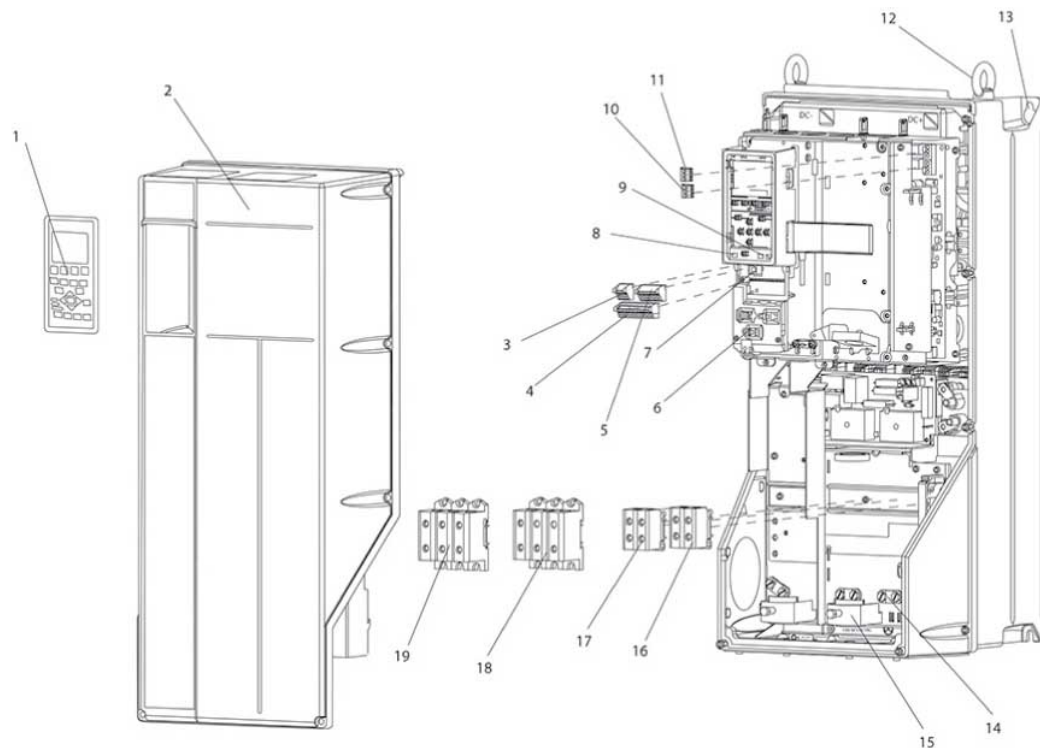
Explosionszeichnung der Rahmengrößen B und C, IP 55, IP 66 UL Typ 3R, 12 und 4X
